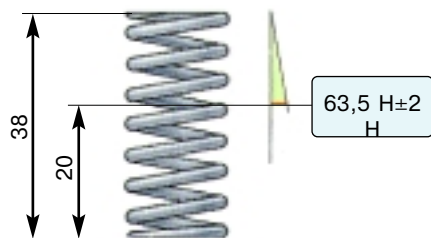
Основные данные для проверки пружины редукционного клапана двигателя мод. 2106-70
